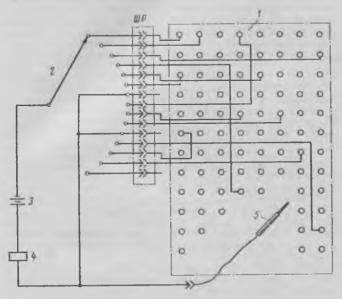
Схема устройства для контроля соединений: 1— рейка зажимов; 2— щетка; 3— источник тока; 4— электромагнит: 5— шуп
